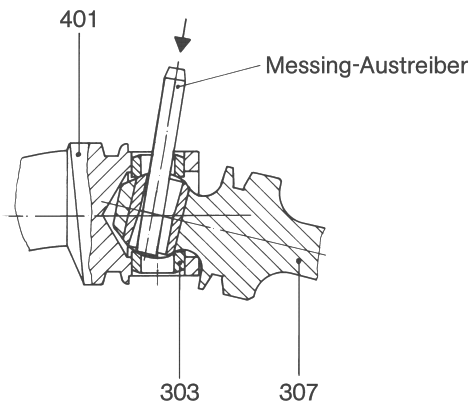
Ausbau der Buchsen für Gelenkbolzen.
